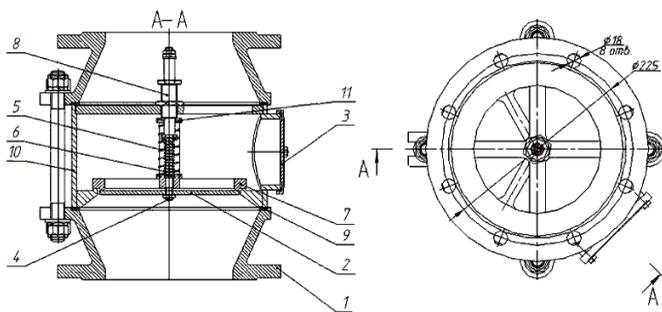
Клапан тип КДЗТ: 1 – корпус; 2 – тарелка вакуума; 3 – крышка смотрового окна; 4 – ось; 5 – пружина клапана давления; 6 – пружина клапана вакуума; 7 – тарелка давления; 8 – регулировочный винт давления; 9 – уплотнение; 10 – обечайка; 11 – шайба опорная
